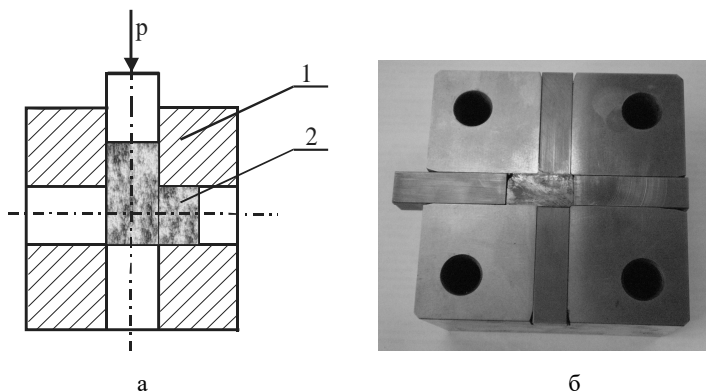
Установка для РКУ-прессования: фото матрицы – а; эскиз штампа – б: 1 – матрица; 2 – образец
